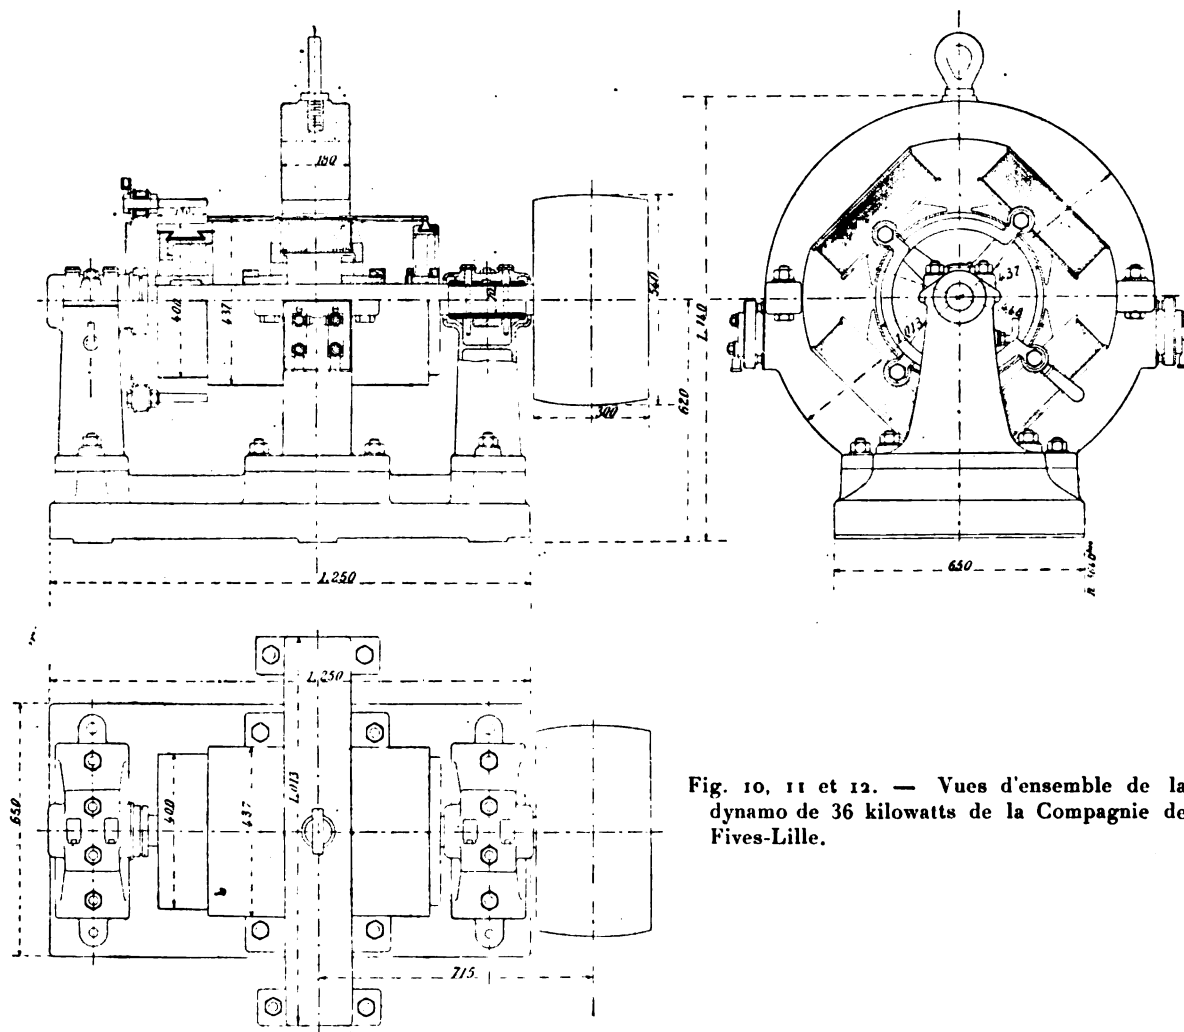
, 11 et 12. — Vues d'ensemble de la dynamo de 36 kilowatts de la Compagnie de Fives-Lille.
